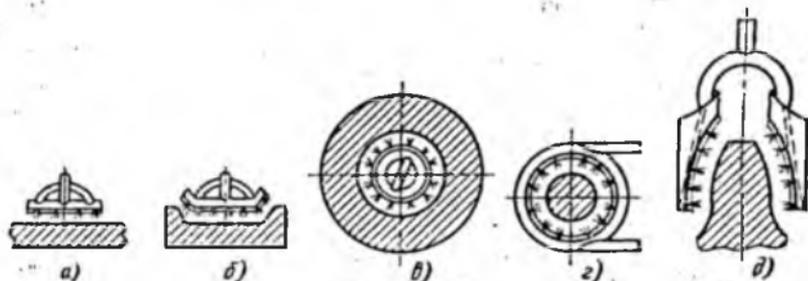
Формы наконечников для закалки газокислородным пламенем: а — плоский; б — для полутавровой поверхности; в — для закалки внутренних поверхностей; г — для цилиндрических тел; д — для закалки одного зуба зубчатого колеса
